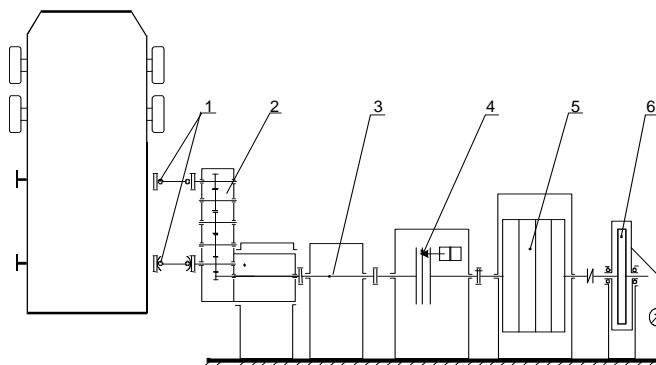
Схема сборки нагружающего устройства для испытаний колёсных БТР (на один борт)
